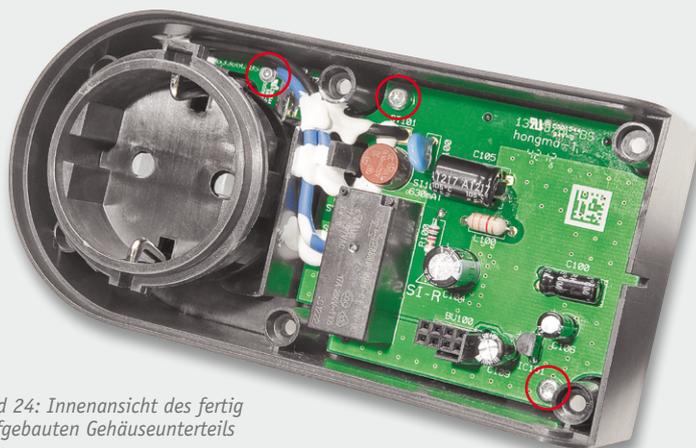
Innenansicht des fertig aufgebauten Gehäuseunterteils
